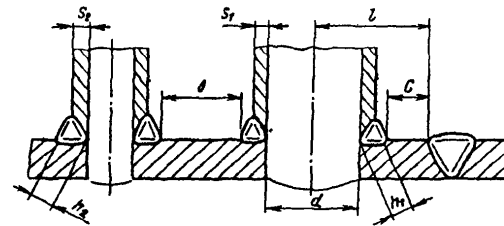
Расположение сварных швов приварки патрубков:
